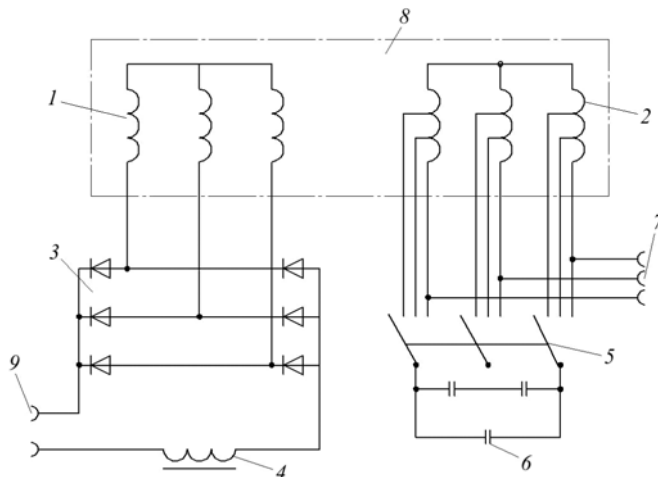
Схема двухобмоточного сварочного генератора Юлке и Дасселя
